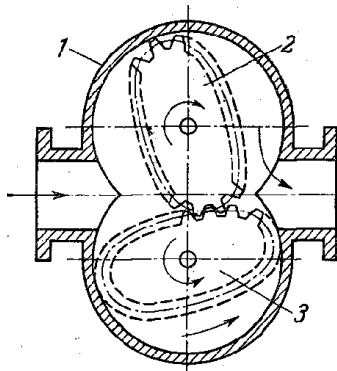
Схема лічильника рідини з овальними шестернями
